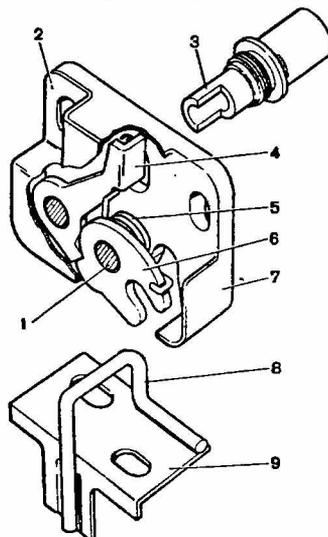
Замок багажника: 1 - ось ротора; 2 - крышка корпуса замка; 3 - удлинитель привода замка; 4 - рычаг; 5 - пружина; 6 - ротор; 7 - корпус замка; 8 - фиксатор; 9 - пластина фиксатора
